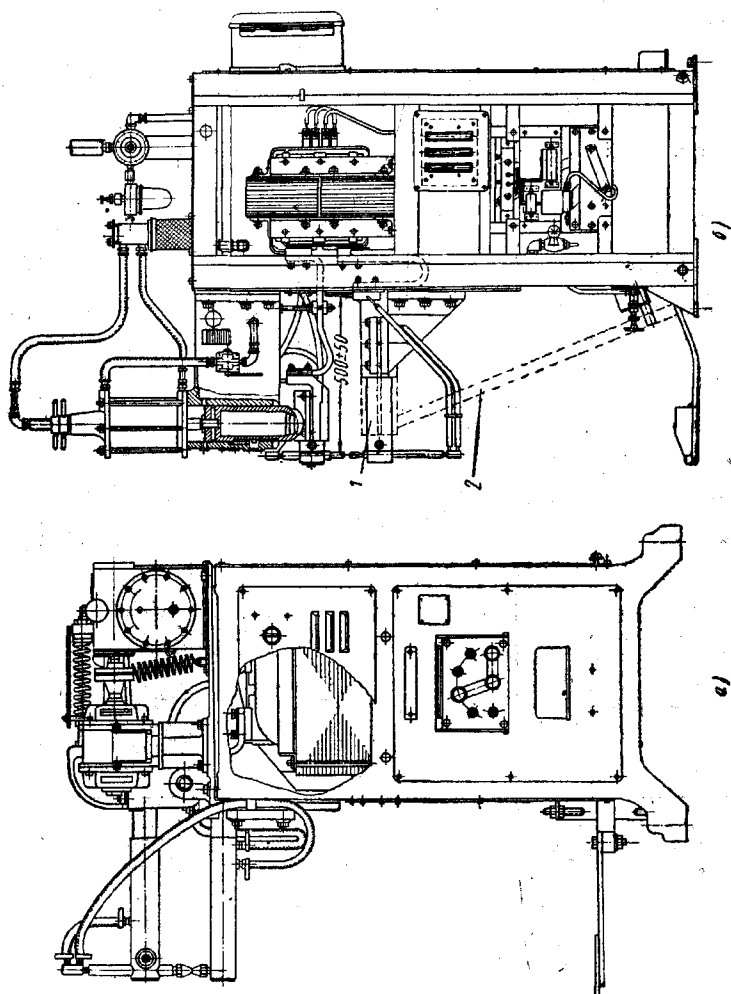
Конденсаторная точечная машина для сварки тонких деталей.
